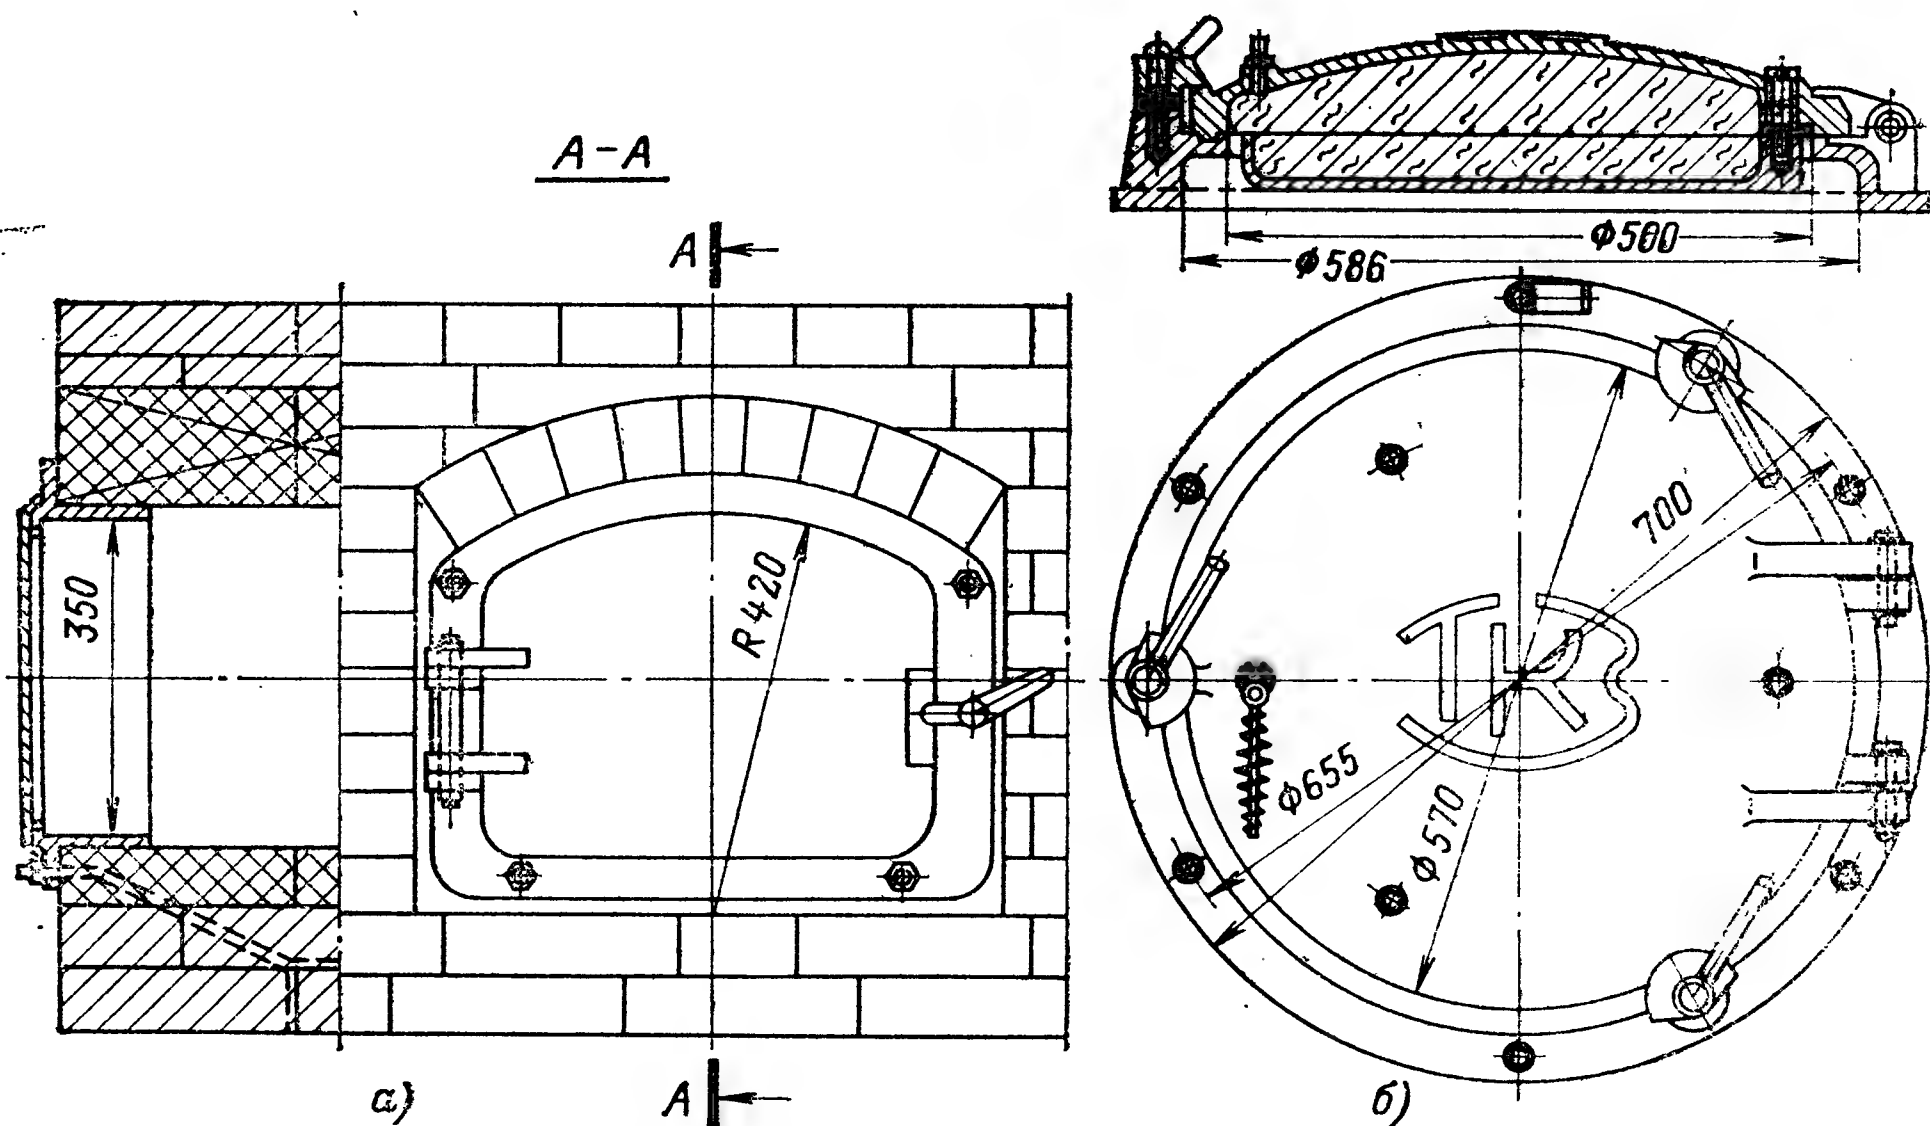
Лазы прямоугольной (а) и круглой (б) формы в обмуровке для осмотра поверхностей нагрева.
